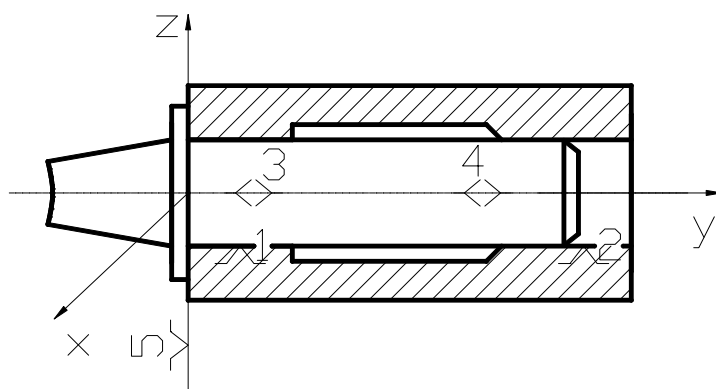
Базування по довгій внутрішній поверхні обертання (з зазором)
